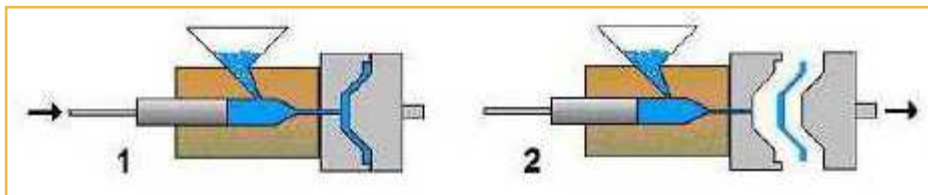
Moldeo por inyección. <http://www.youtube.com/watch?v=Gm6HgSGT6DM>
